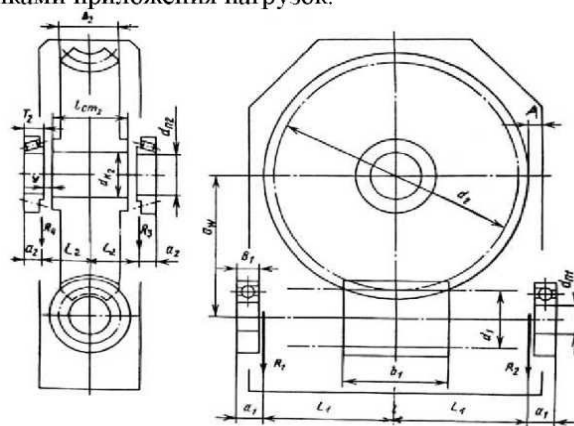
Схема предварительной компоновки одноступенчатого червячного редуктора
